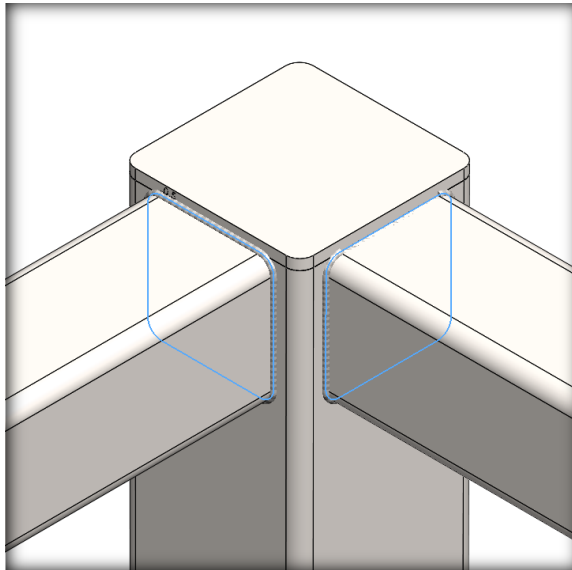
Detalle 1: Encuentro perfiles #120 con perfil #170
